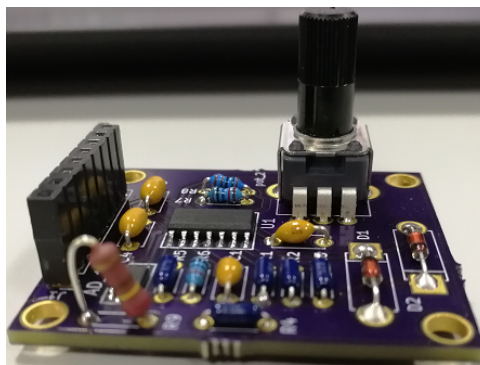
PCB fabricada por Osh Park con los componentes soldados en cara superior. (vista lateral)
